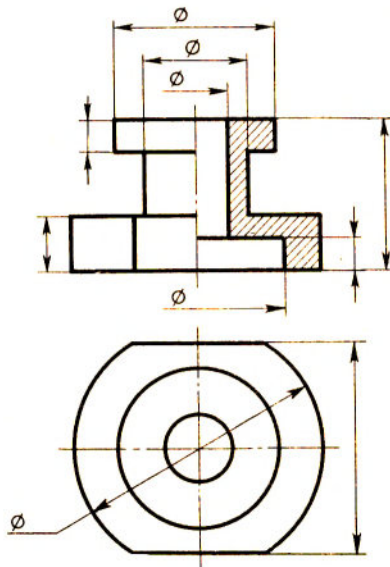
Нанесение размеров на чертеже детали, содержащем разрез
